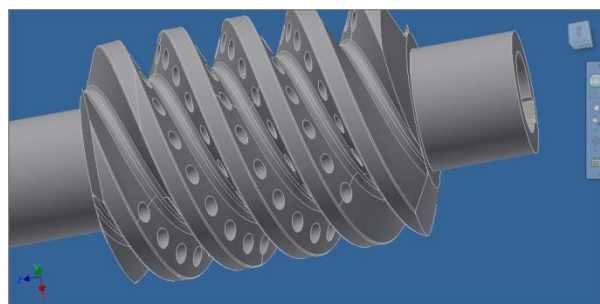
Трехзаходный червячный шевер со сферическими канавками
